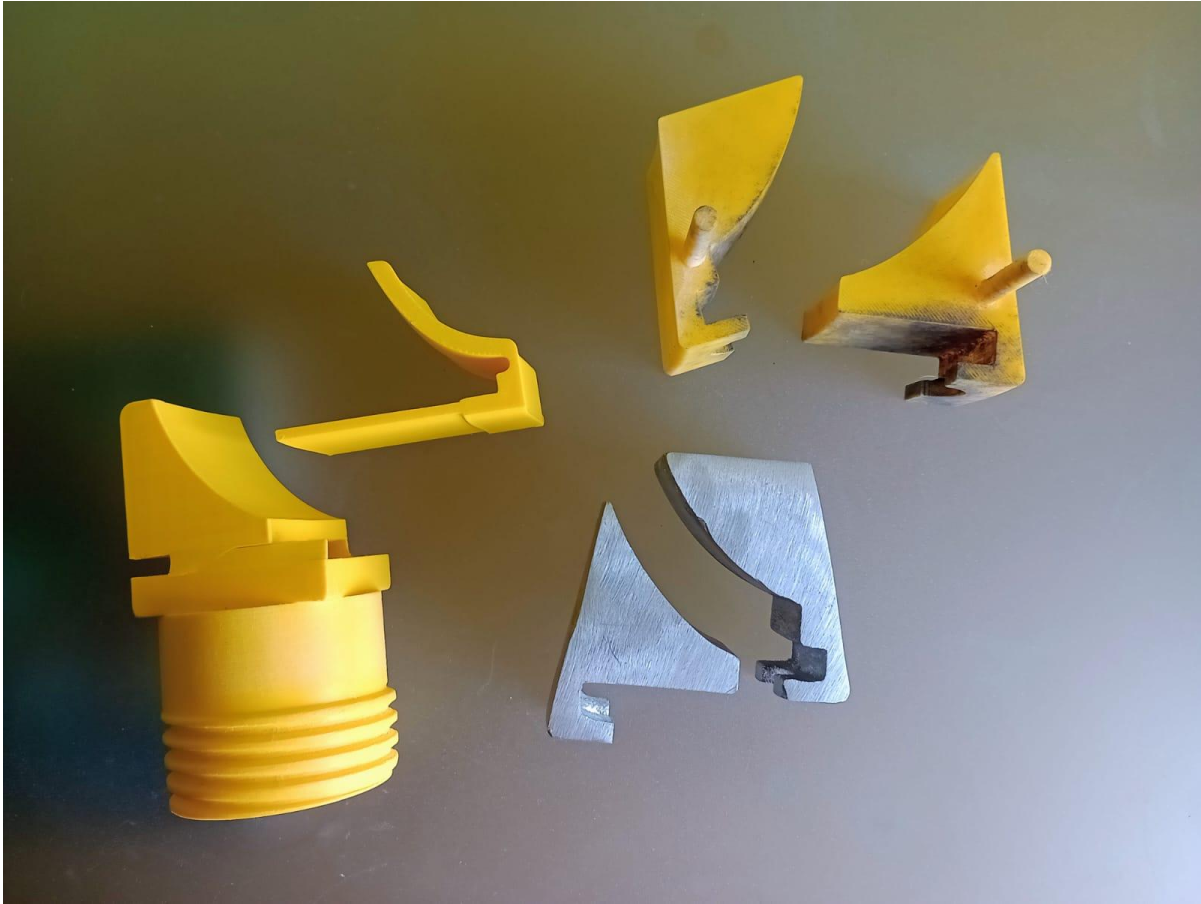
Cabezas carcasa versión 1 y 2 CHECKTOOL
